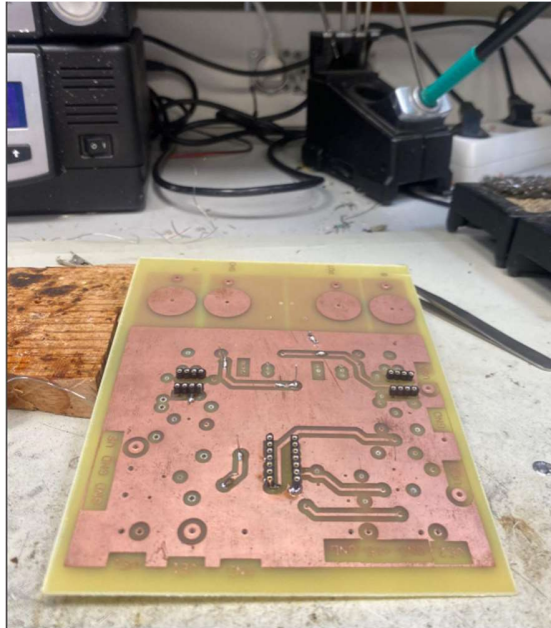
Imagen de como quedan los componentes soldados.
